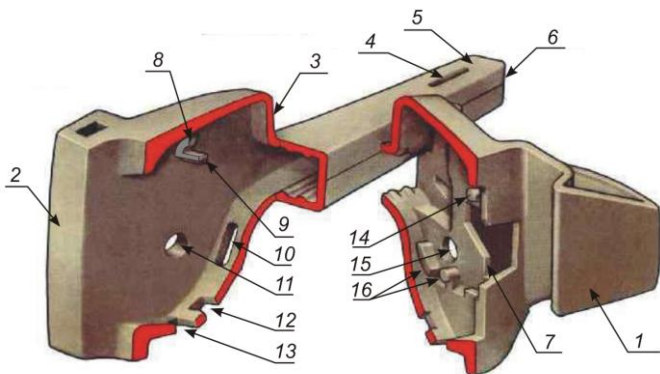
Карман корпуса автосцепки СА-3:
